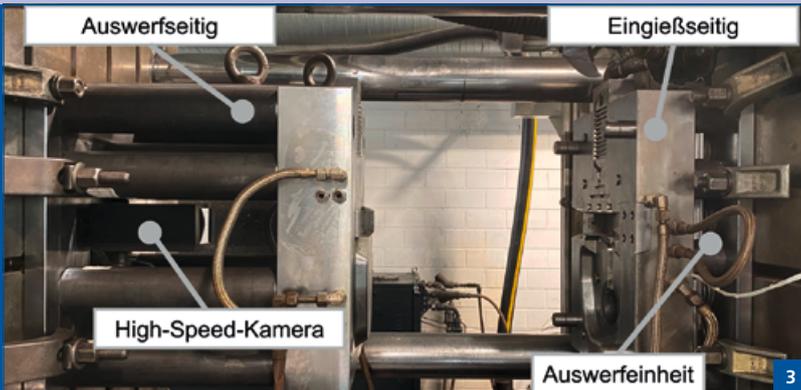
Seitenansicht des Druckgießwerkzeugs mit optischer Zugänglichkeit und High-Speed-Kamera im Auswerferkasten
